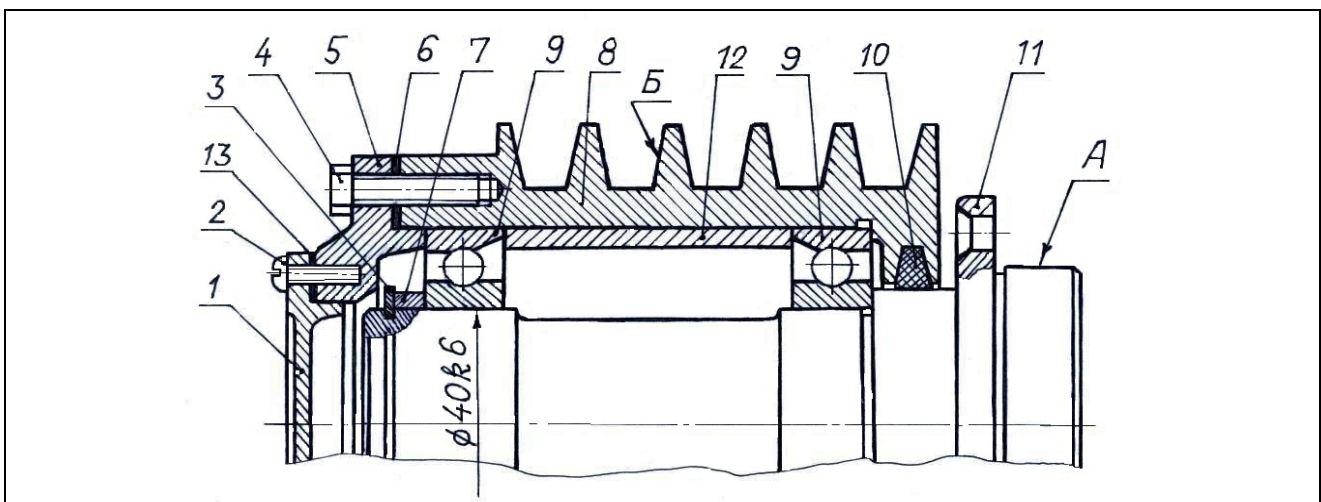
Сборочный чертеж ступицы шкива вентилятора:
